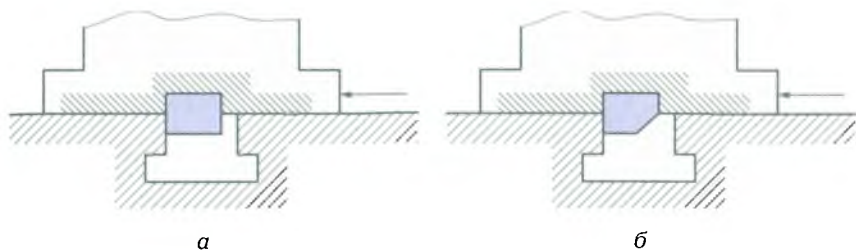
Конструкции шпонок, способствующие повышению точности установки приспособлений:
